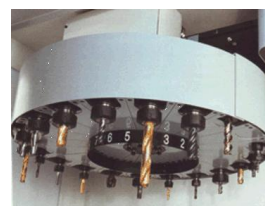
Дисковый инструментальный магазин с вертикальной осью фрезерный станка мод. ЛФ260МФЗ
